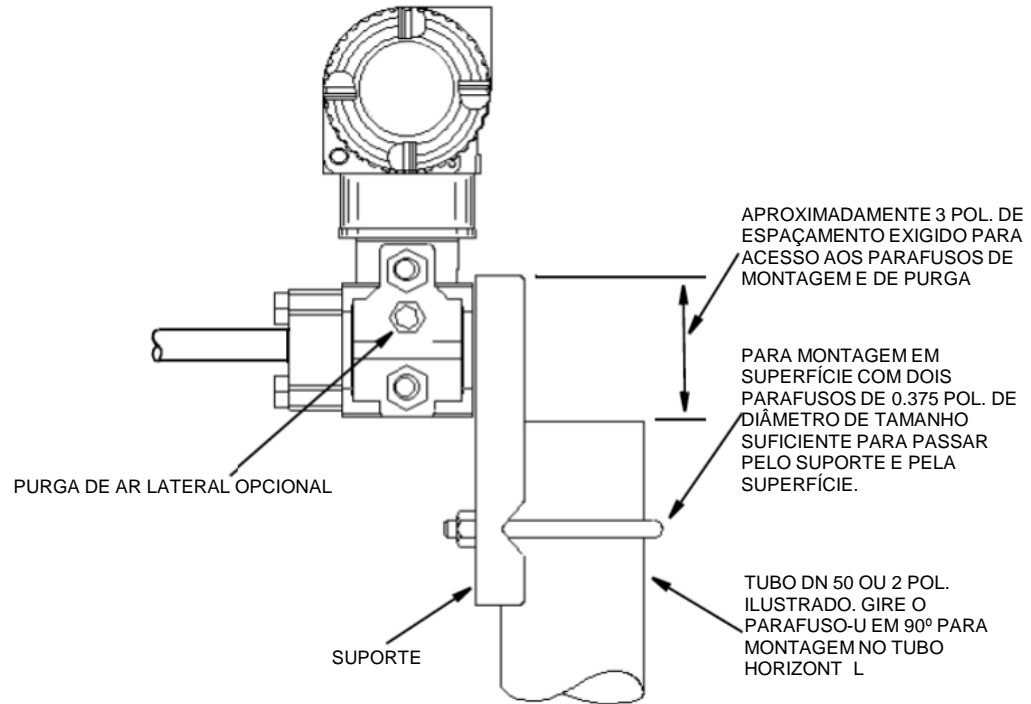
Transmissor Montado em Tubo ou em Superfície Utilizando um Suporte Padrão
